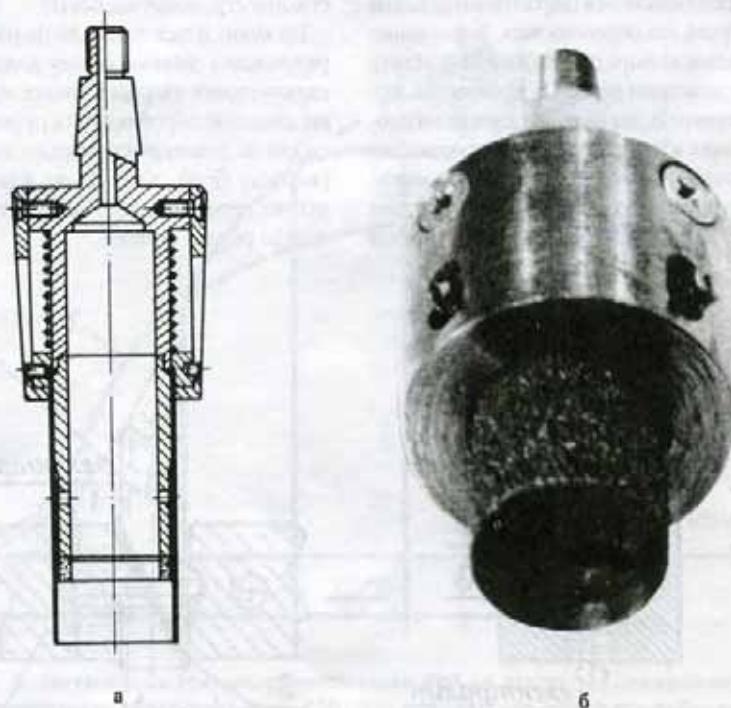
«Рубашочне свердло»: а – схема конструкції, б – інструменти
